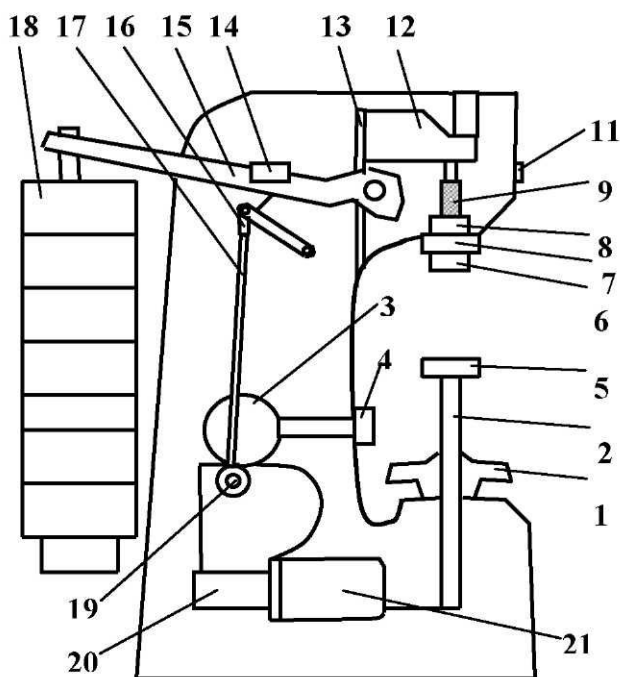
Схема прибора для определения твердости по Бринеллю
